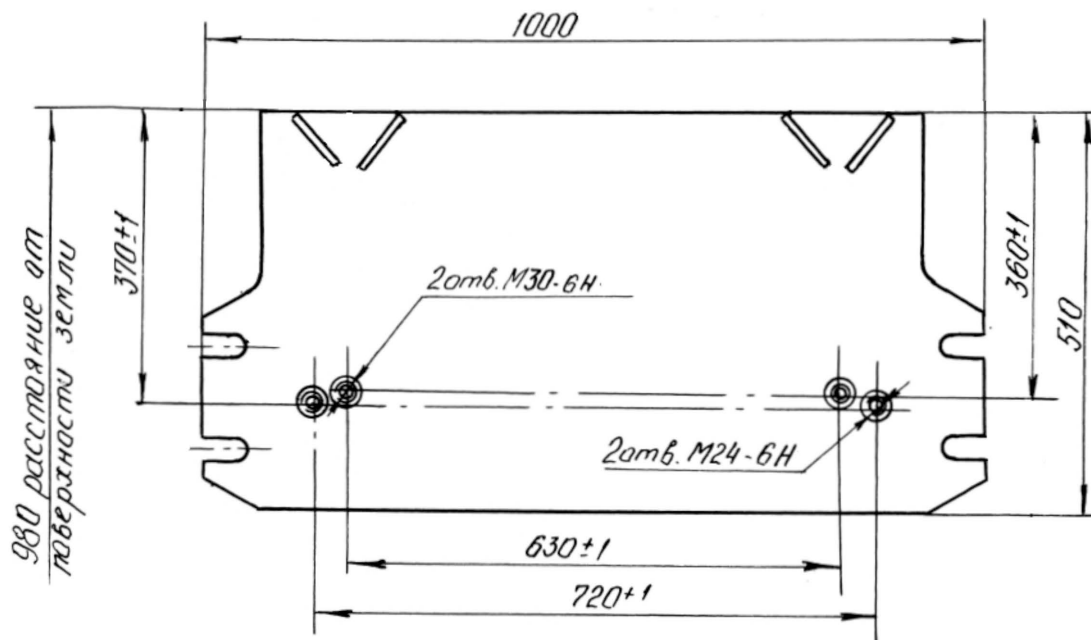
Присоединительные размеры к боковому навесному устройству
